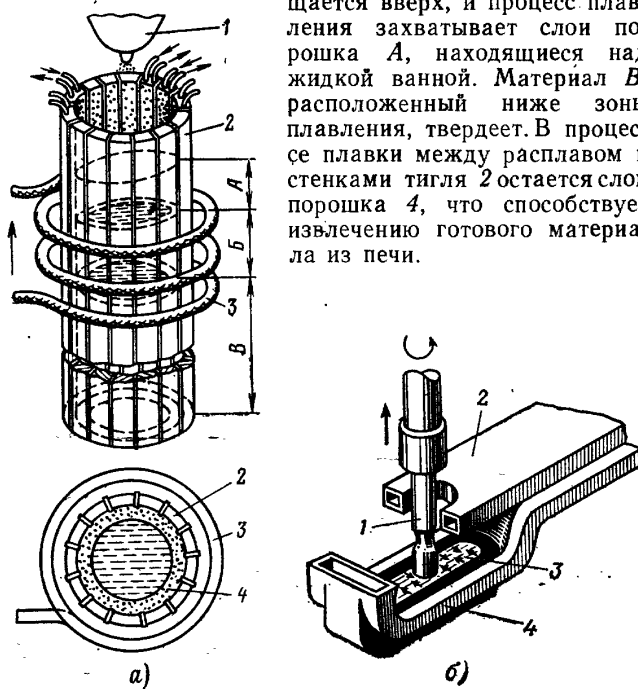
Тигли для плавки огнеупоров. а — трубчатый тигель для непрерывной плавки; б — индуктор-тигель с вертикальным витком для выращивания монокристаллов из расплава.
